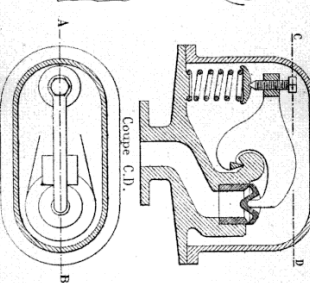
Soupape de sûreté à ressort Coupe A.B.
